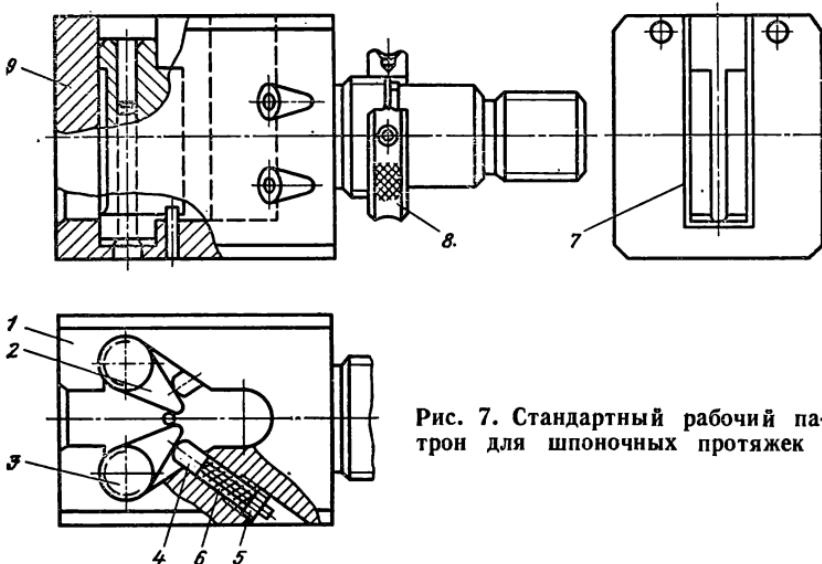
Стандартный рабочий патрон для шпоночных протяжек
